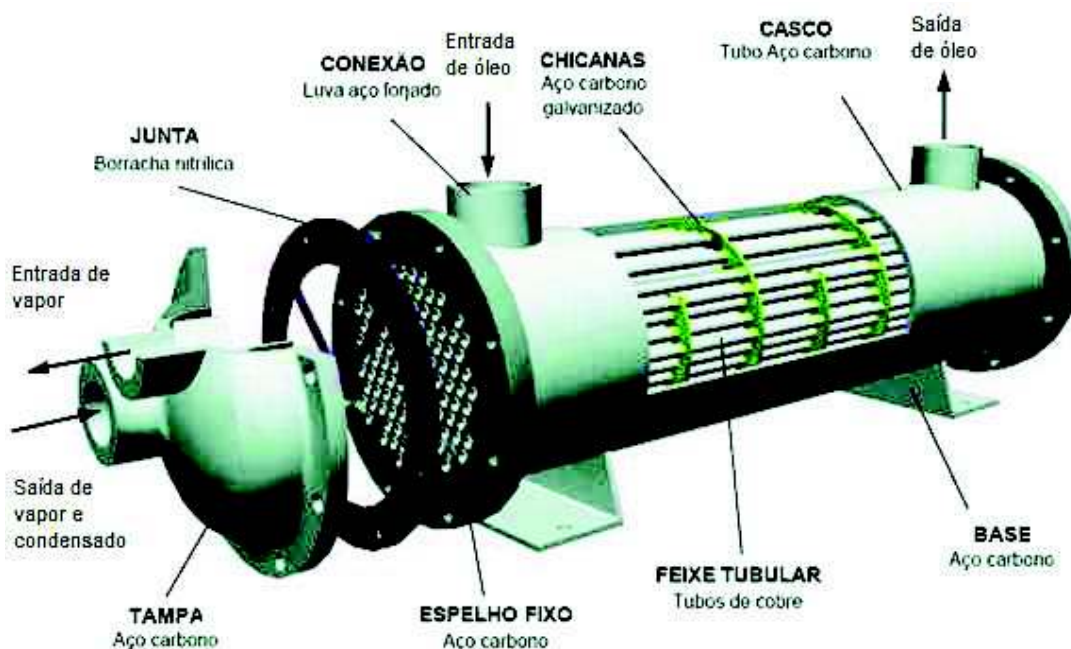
Vista explodida de trocador de calor do tipo casco e tubos [3].
